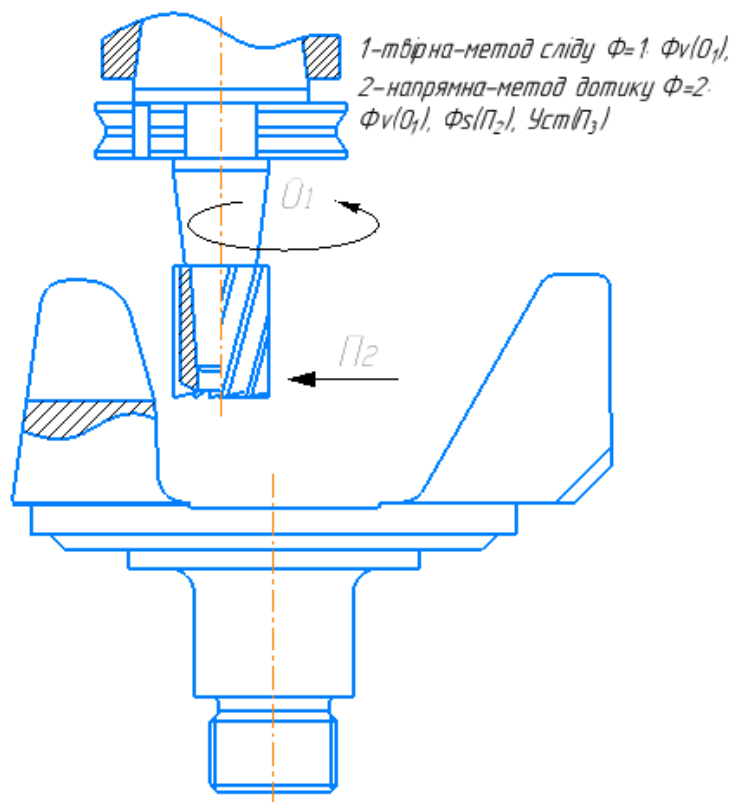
Схема формування при фрезеруванні циліндричною фрезою
